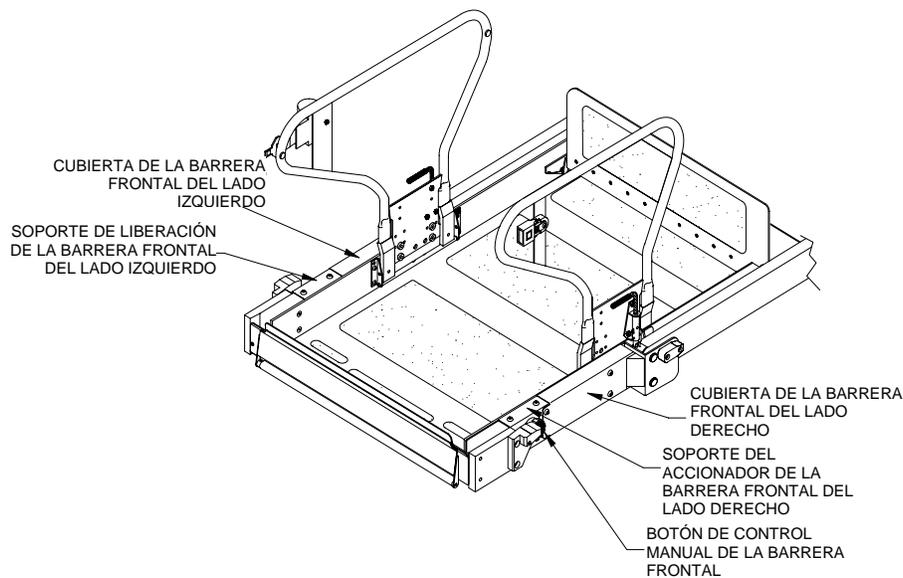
CUBIERTAS DE ACCESO PARA EL MECANISMO DE LA BARRERA FRONTAL
